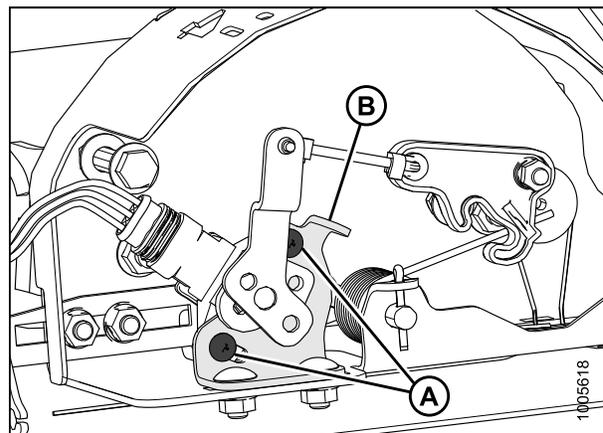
Ensemble de capteur de hauteur automatique de plateforme pour moissonneuses-batteuses Lexion
